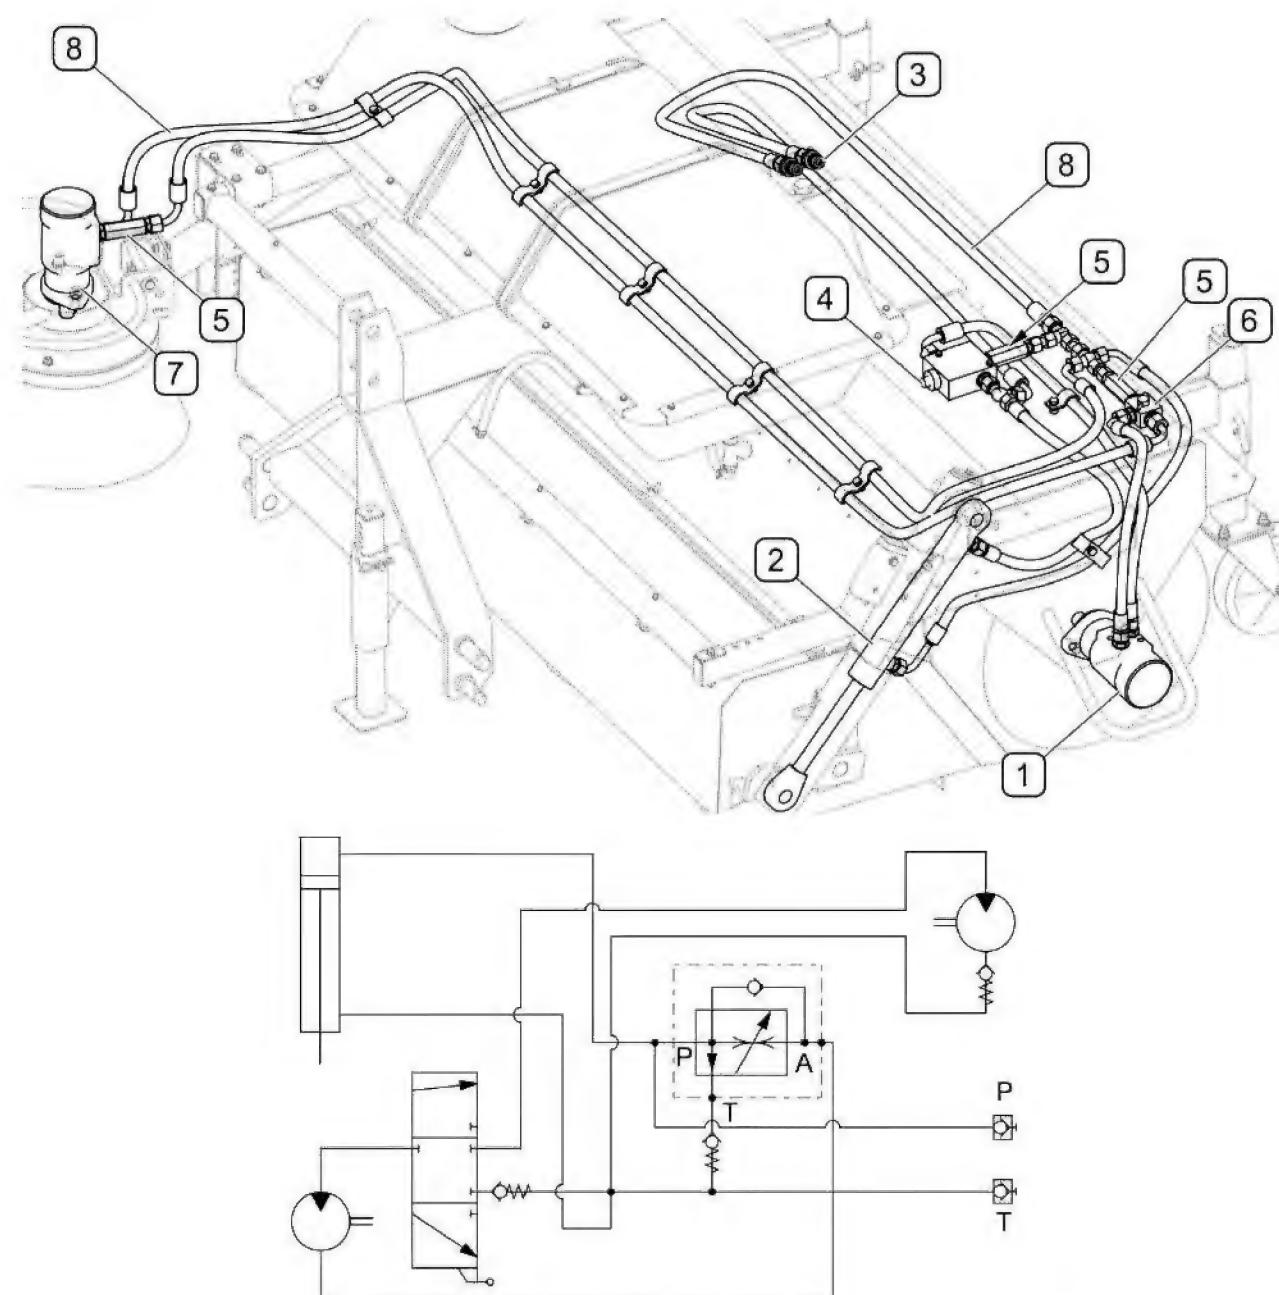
A Construction du circuit hydraulique des balayeuses ZM-1600-01 et ZM-1600-03
